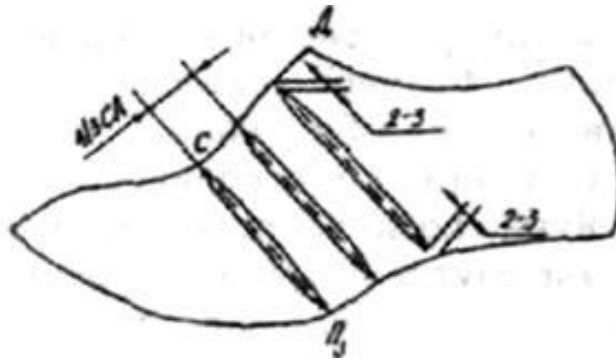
Розтин зліпку бокової поверхні колодки
